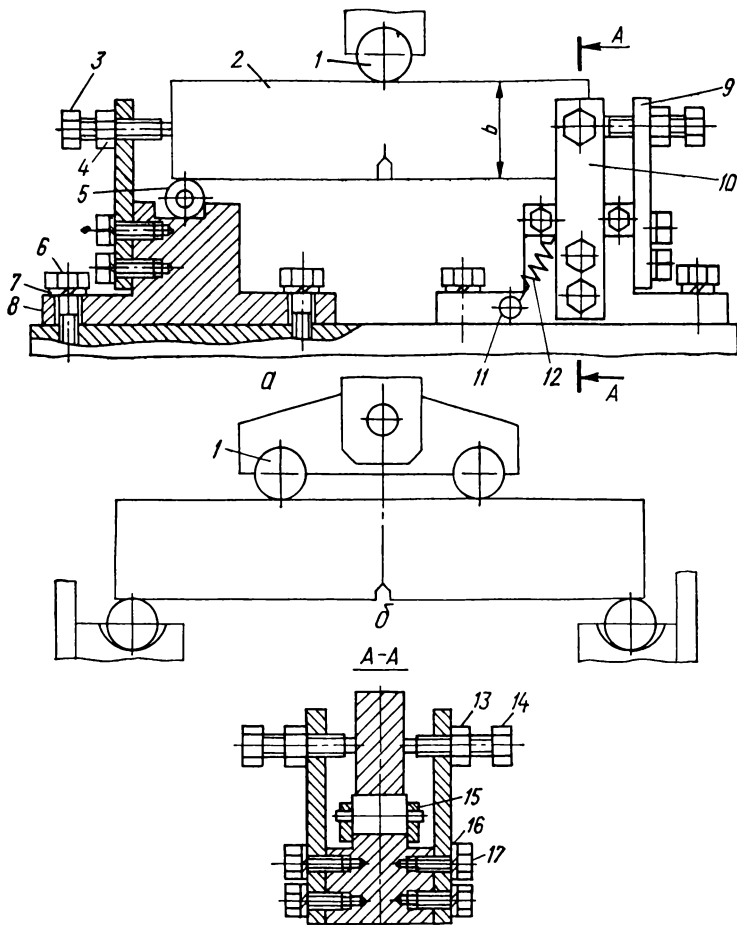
Приспособление для нагружения образцов по схеме трехточечного (а) и четырехточечного (б) изгибов (схемы 14 а, б в табл 5.1): 1 — ролик нагружающий; 2 — образец; 3, 14 — болт установочный; 4, 13 — гайка; 5 — ролик опорный. 6, 17 — болт 7, 16 — шайба; 8 — корпус основы; 9 — пластина торцевая; 10 — пластина боковая; 11 — винт; 12 — пружина; 15 — пластина ограничительная.
